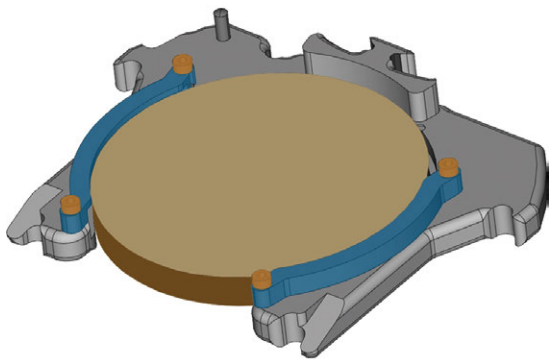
FERMETURE DES CROCHETS DE FIXATION DU CADRE DE PIÈCES BRUTES
